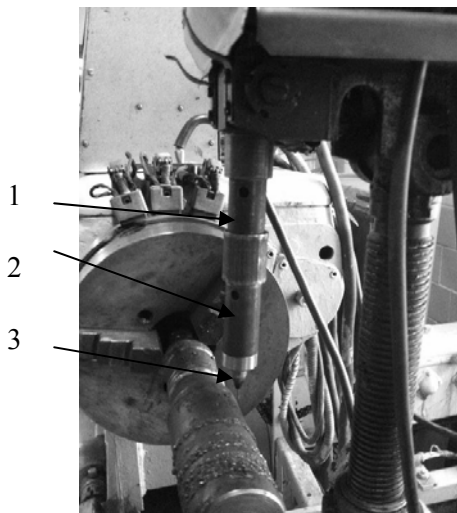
Наплавочная головка для ремонтных мастерских: 1 – бункер для клеевого вещества; 2 – бункер для порошка; 3 – токоподводящий мундштук
